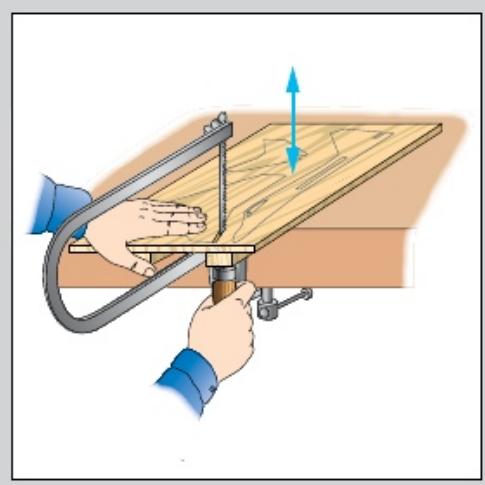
Выпиловочный столик: 1 – верстак; 2 – струбцина; 3 – дощечка
